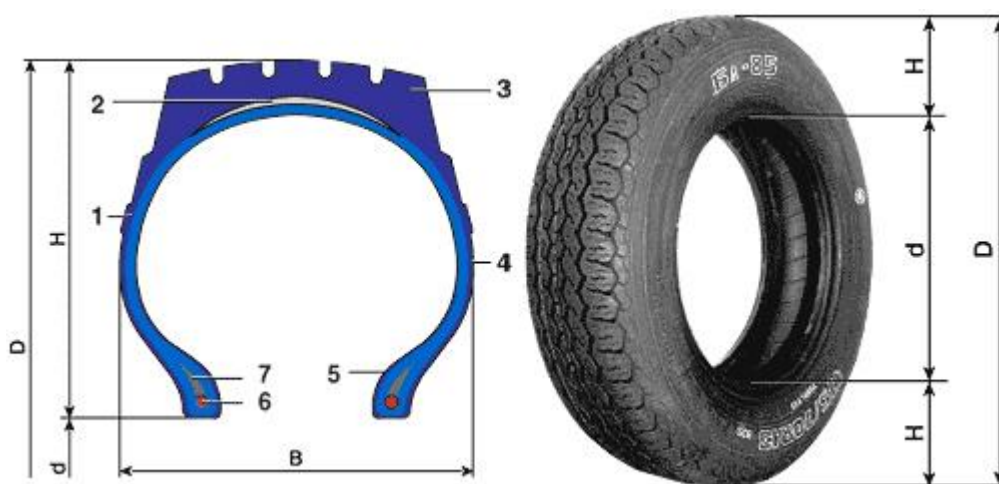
Конструктивные элементы и основные размеры шин:
